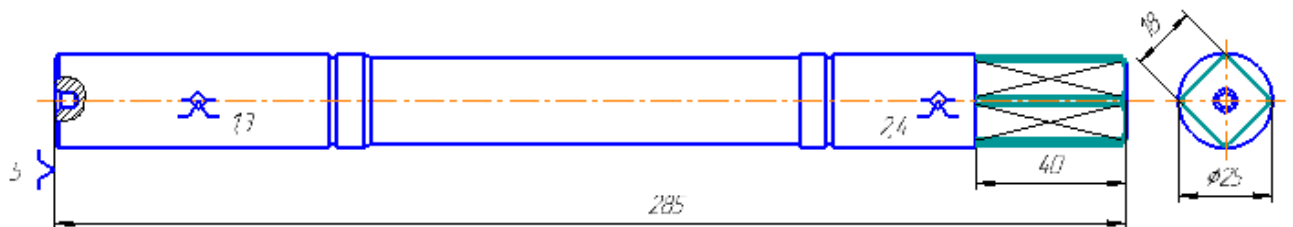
Обробка деталі при фрезерній операції.
